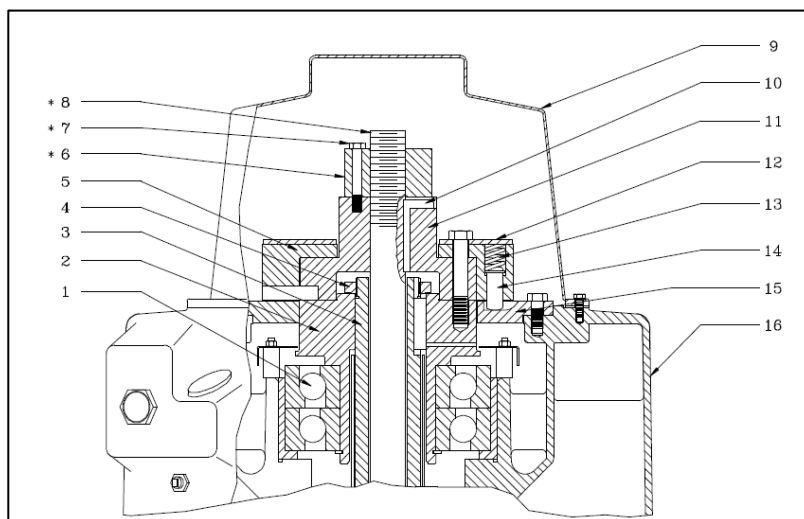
Despiece del Trinquete de Motor Eléctrico.
